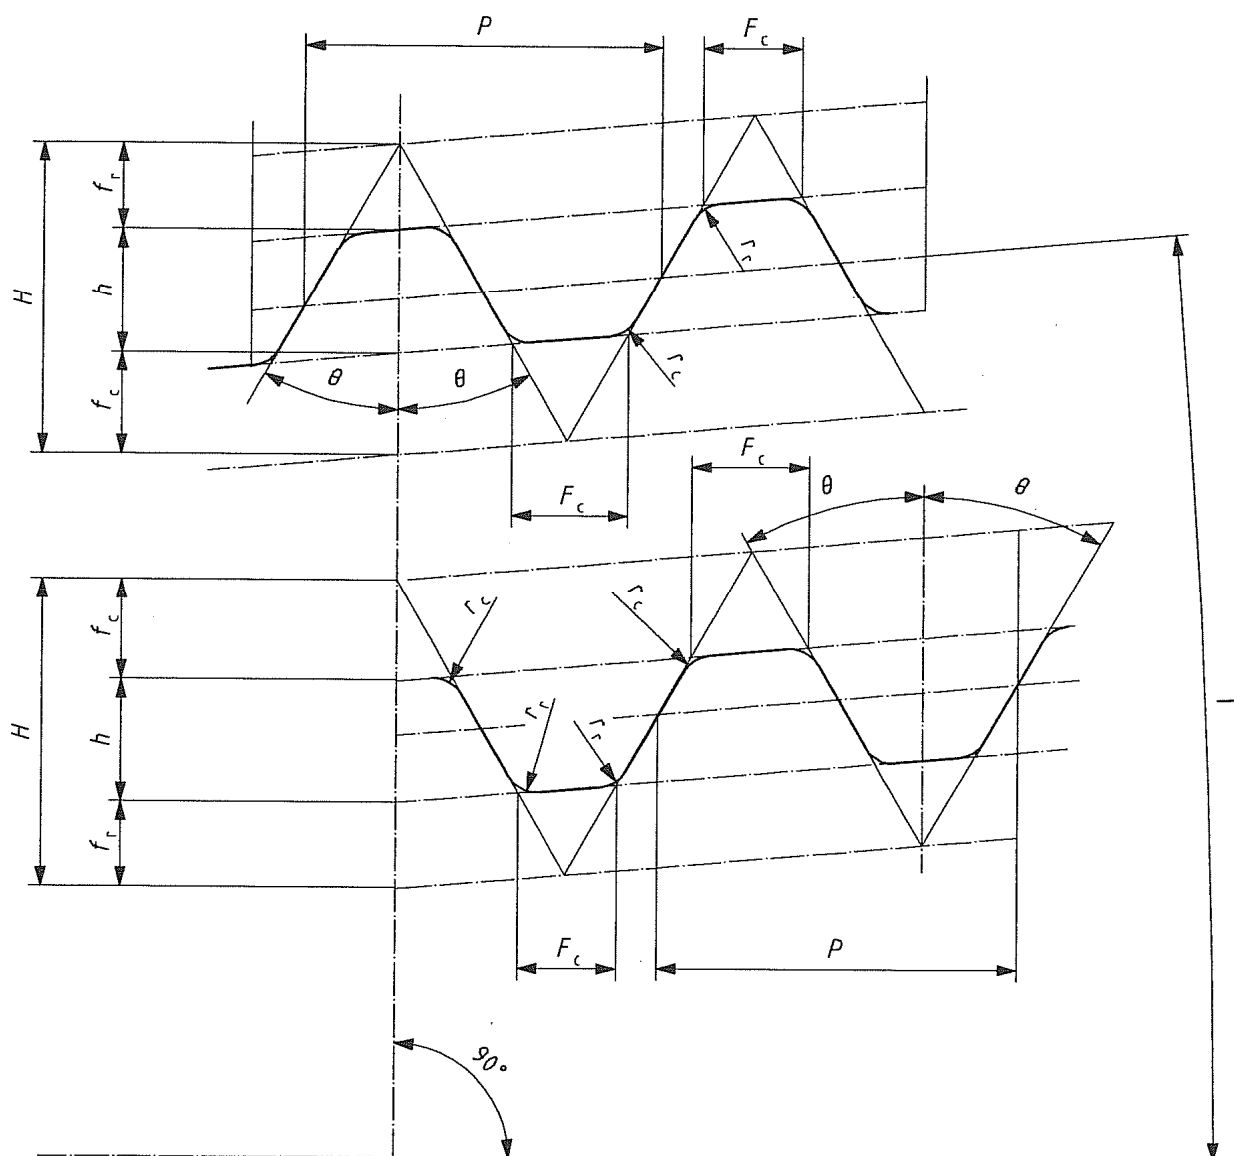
Профили резьбы изделий V-038R (a), V-040, V-050 (b)
